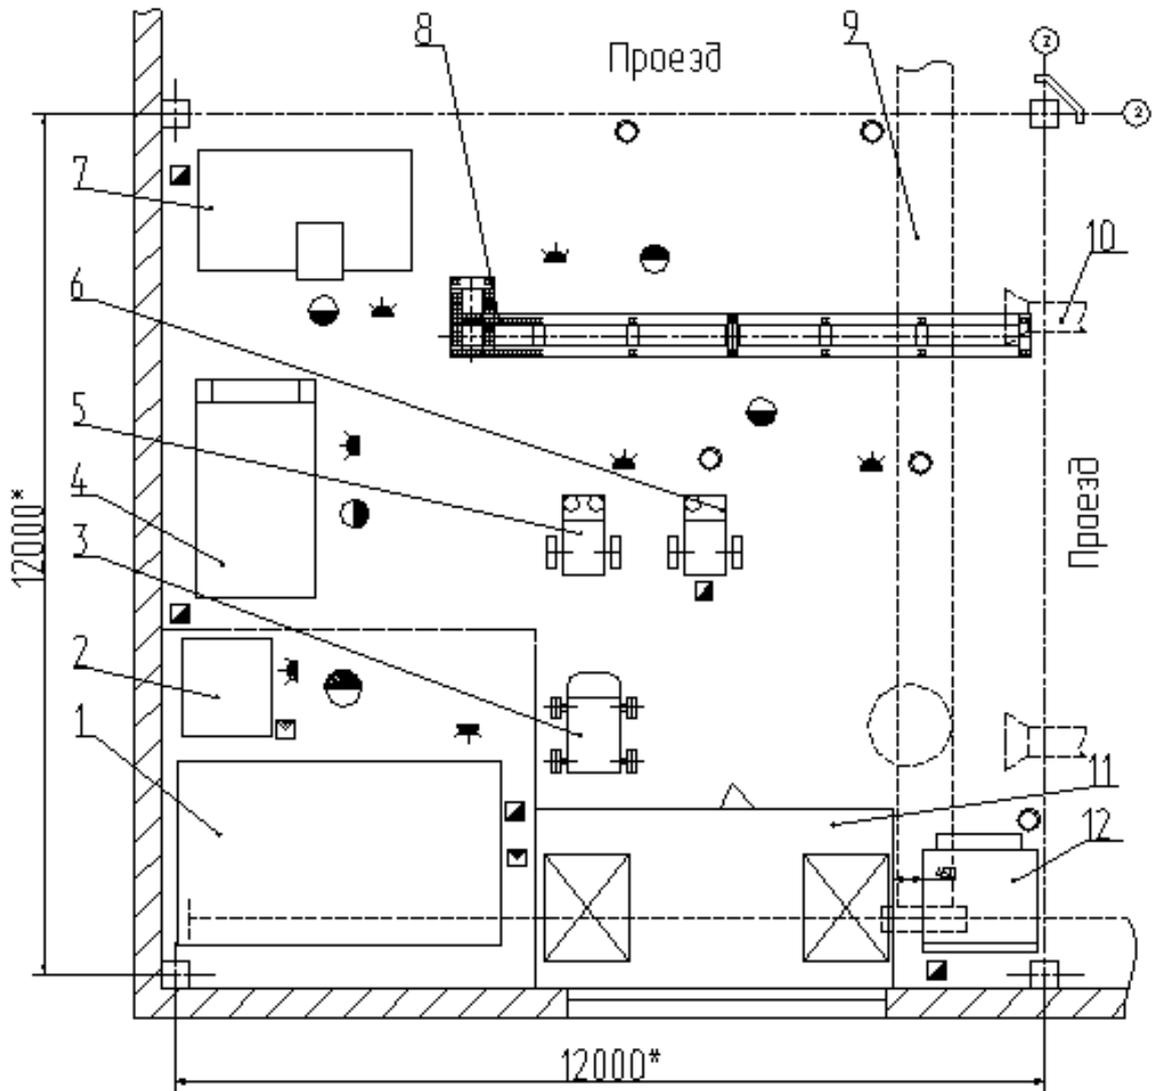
Общий вид участка сварки труб
